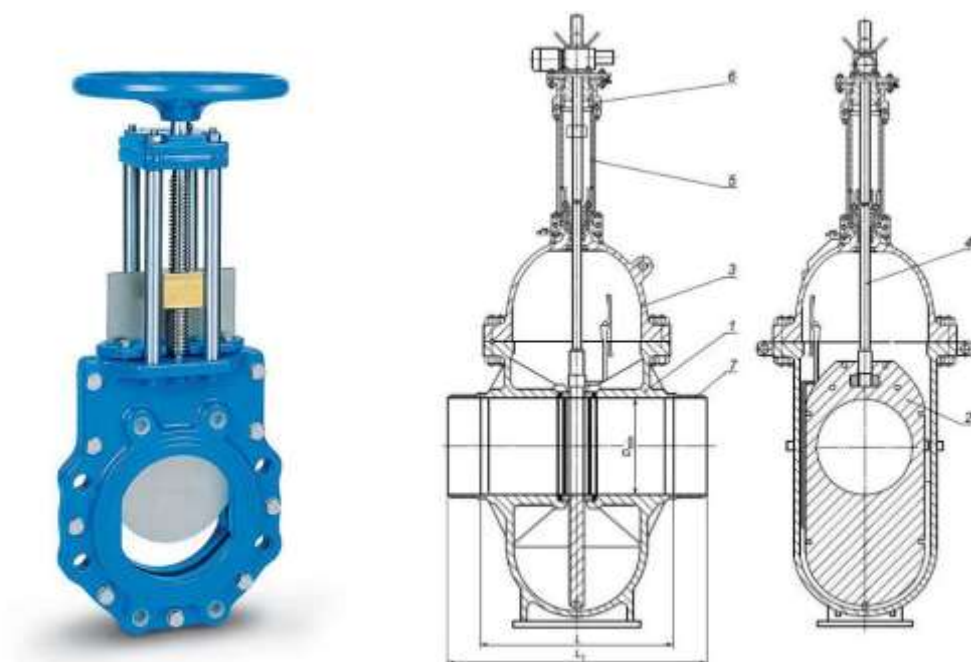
Внешний вид и чертеж задвижки и ее основные части:
